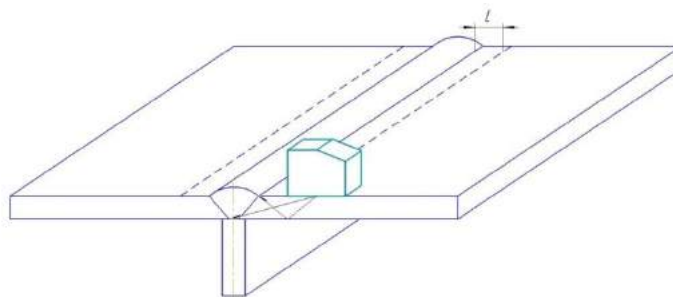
Схема прозвучивания ФР сварного шва № 2:
